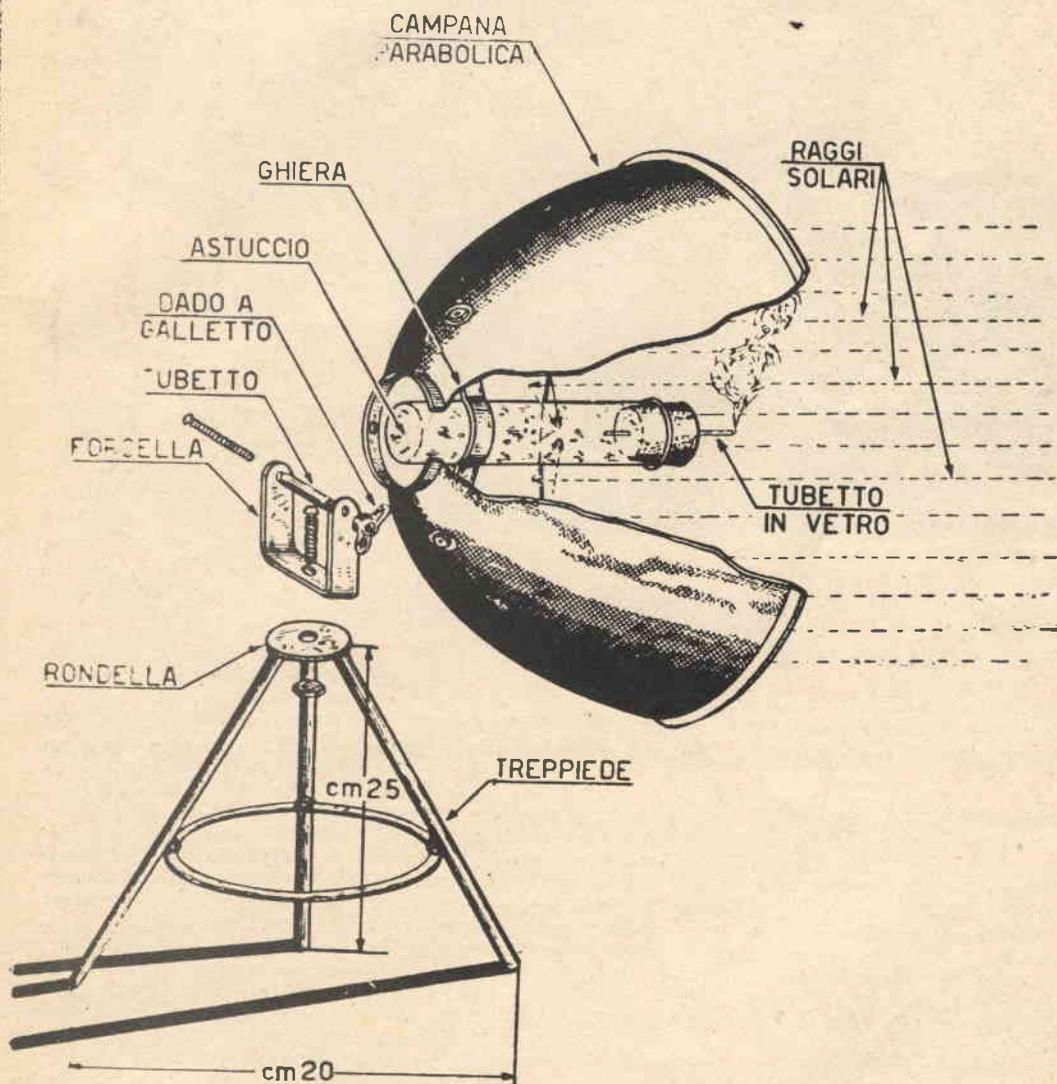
SEZIONE DELLA CAMPANA PARABOLICA
